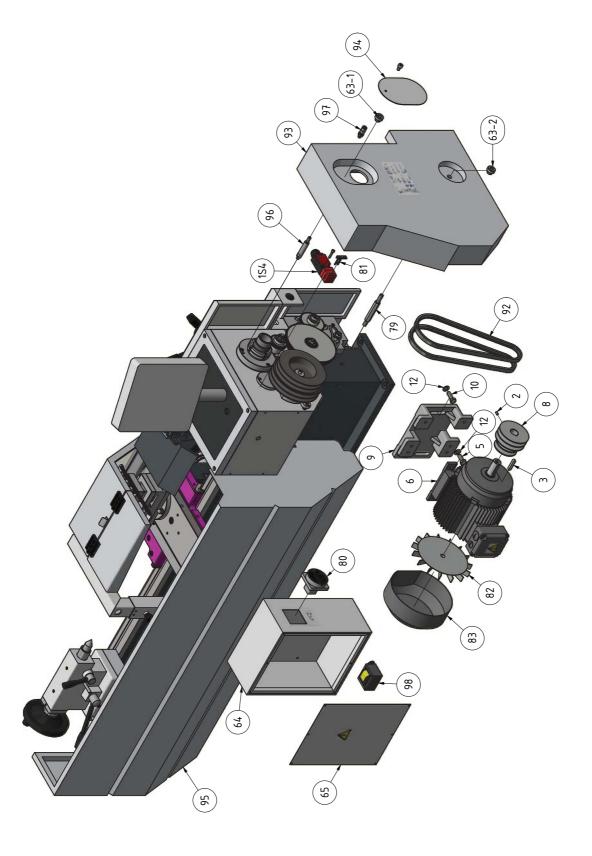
Maschinenbett 1-2 - Lathe bed 1-2
